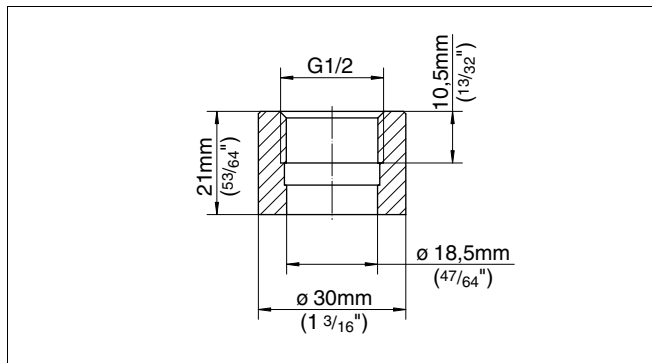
Размеры приварного штуцера G½ А по ISO 228-1
